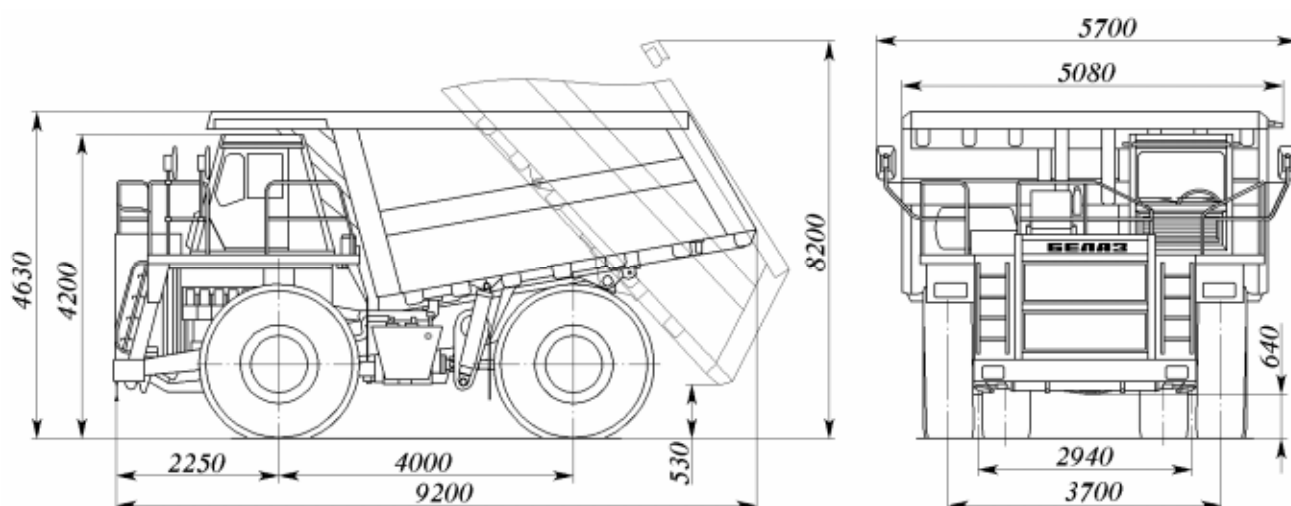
Самосвал-углевоз БелАЗ-7555D. Габаритные размеры
